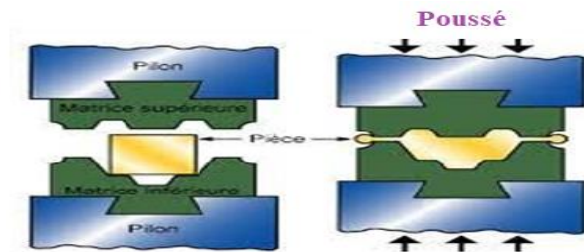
Schéma d'élaboration par forgeage (pièces forgées).
